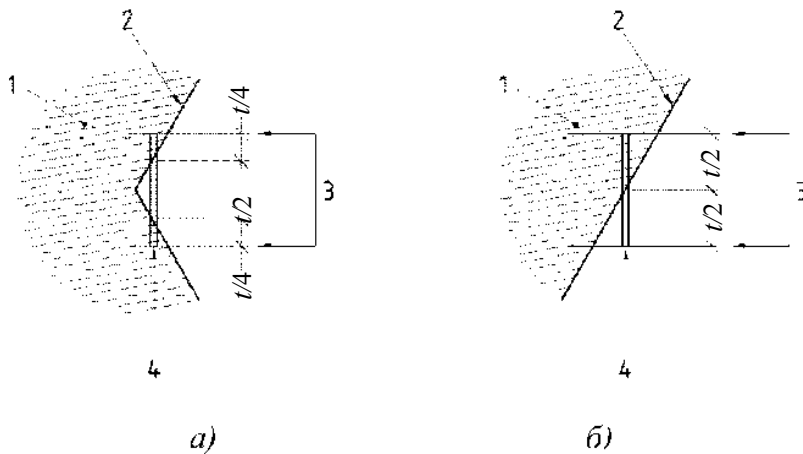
Розмітка положення надрізів зразків з V-подібним надрізом по лінії сплавлення: *a* — симетричне оброблення; *б* — несиметричне оброблення; 1 — метал шва; 2 — лінія сплавлення; 3 — розташування бокових поверхонь зразка; 4 — розташування надріза.
